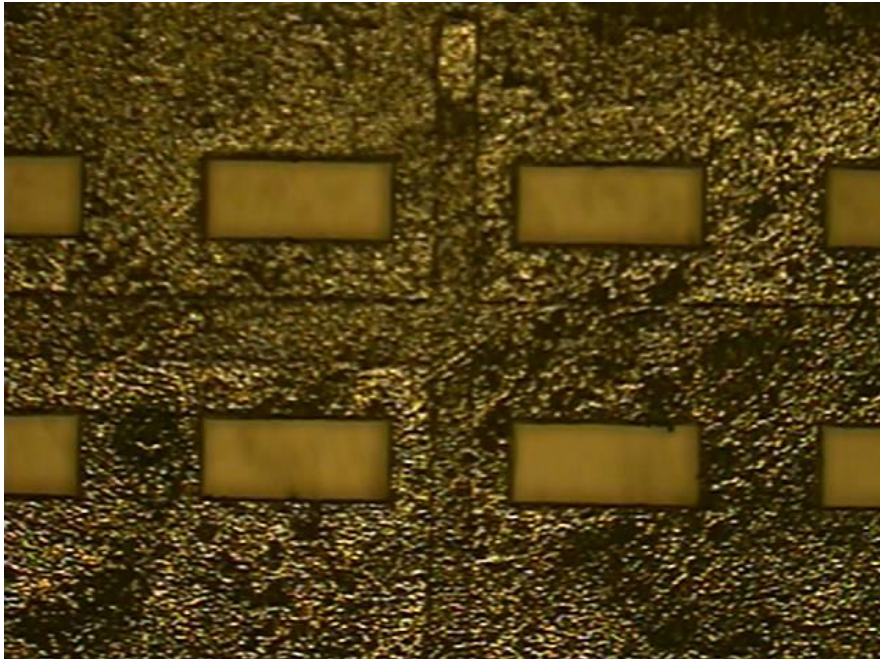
Slots y costillas bajas con 160 pasadas de excavado
